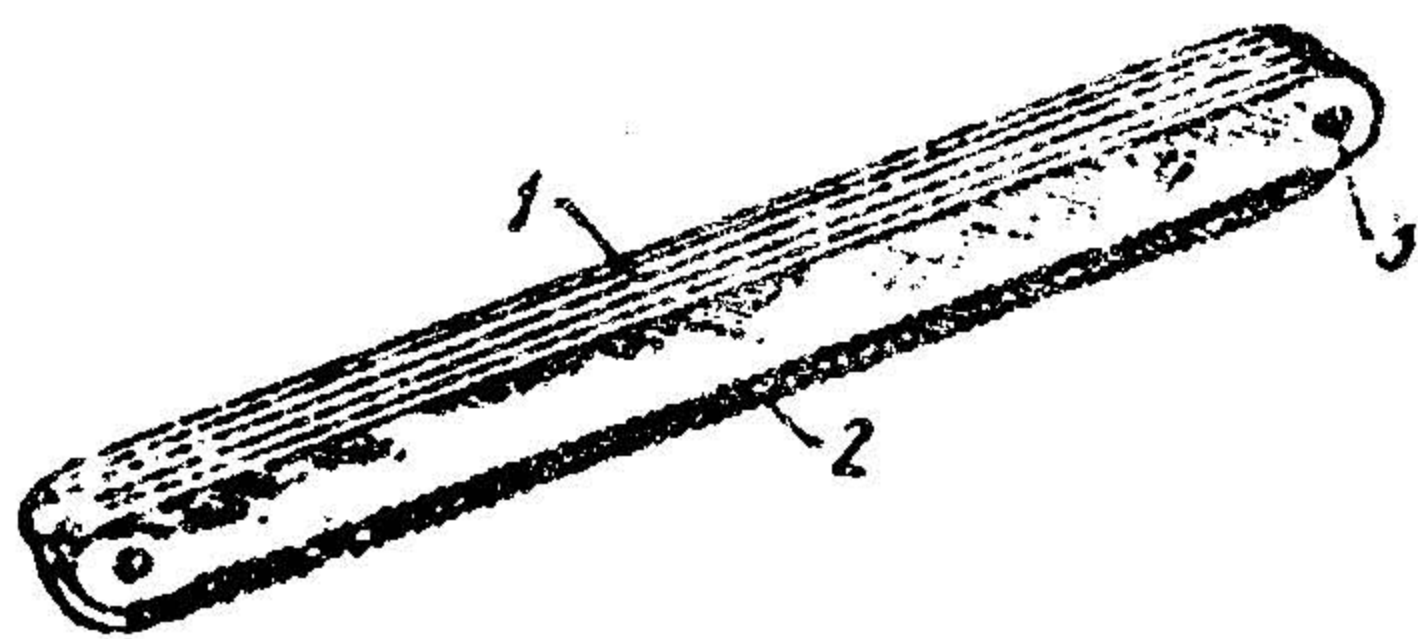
Пакет ножовочных полотен: 1 — полотна; 2 — средняя ножовка; 3 — заклепки
